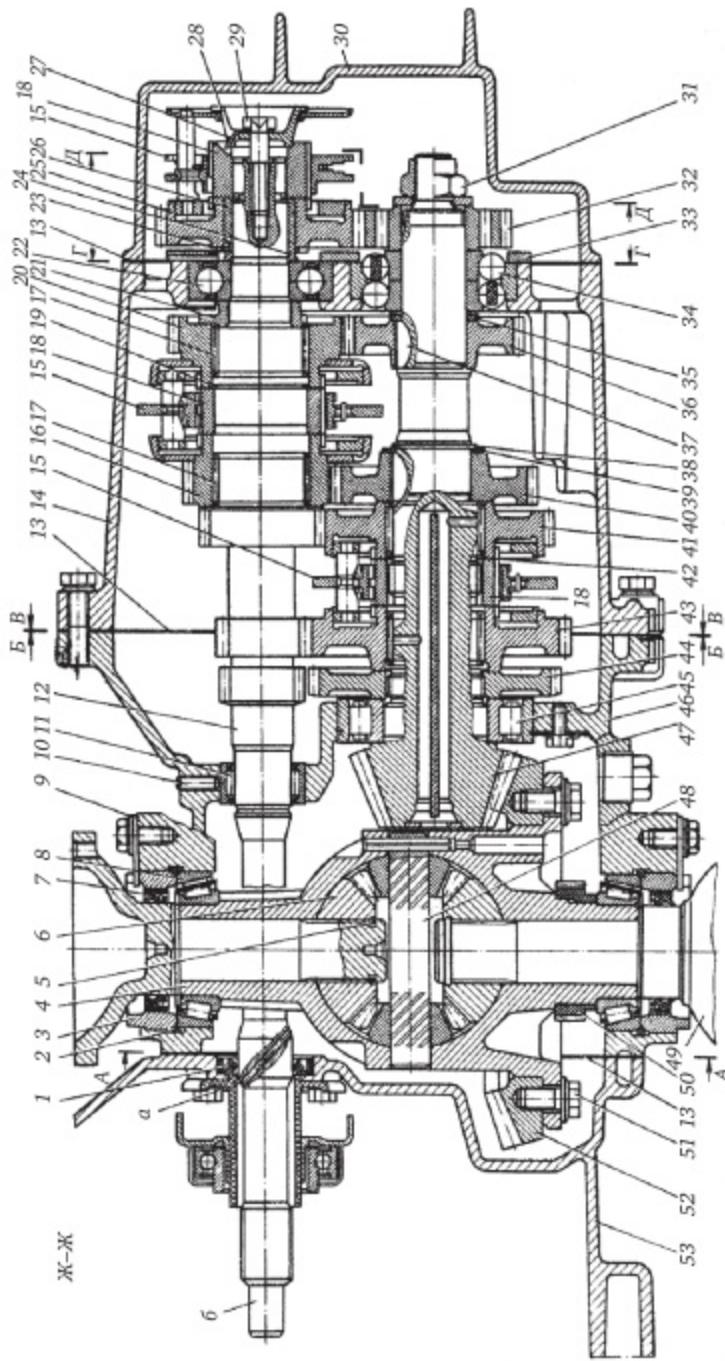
а. Конструкция 2-вальевой 5-ступенчатой коробки передач переднеприводного автомобиля с продольным силовым агрегатом
